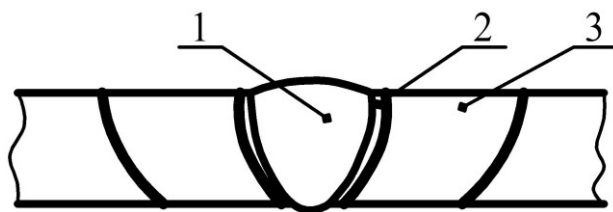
Схема будови зварного з'єднання: 1 – зварний шов;
